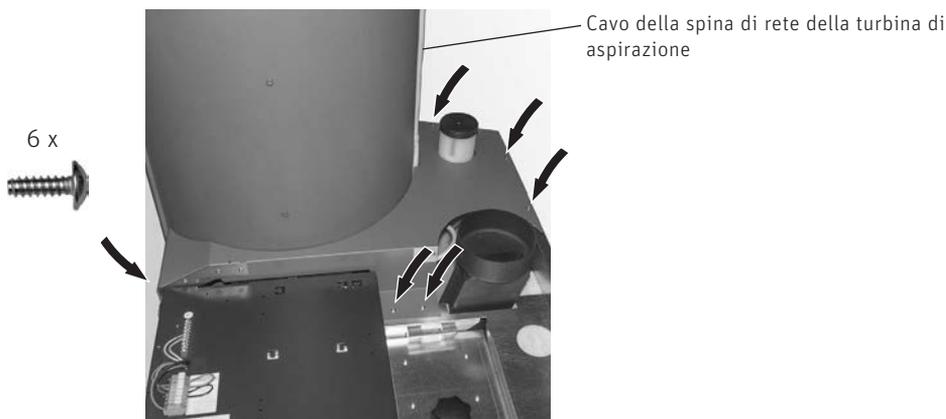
Fissare il rivestimento con 6 viti autofilettanti
